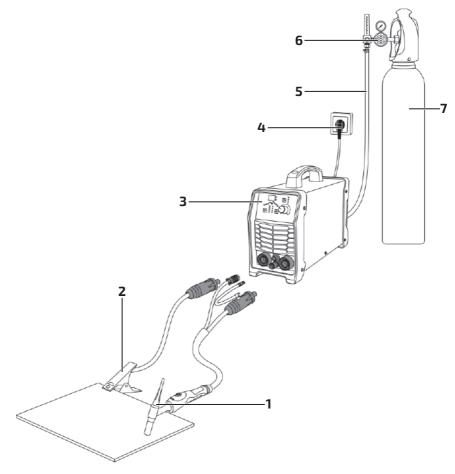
Схема подключения оборудования для TIG Cold сварки.
